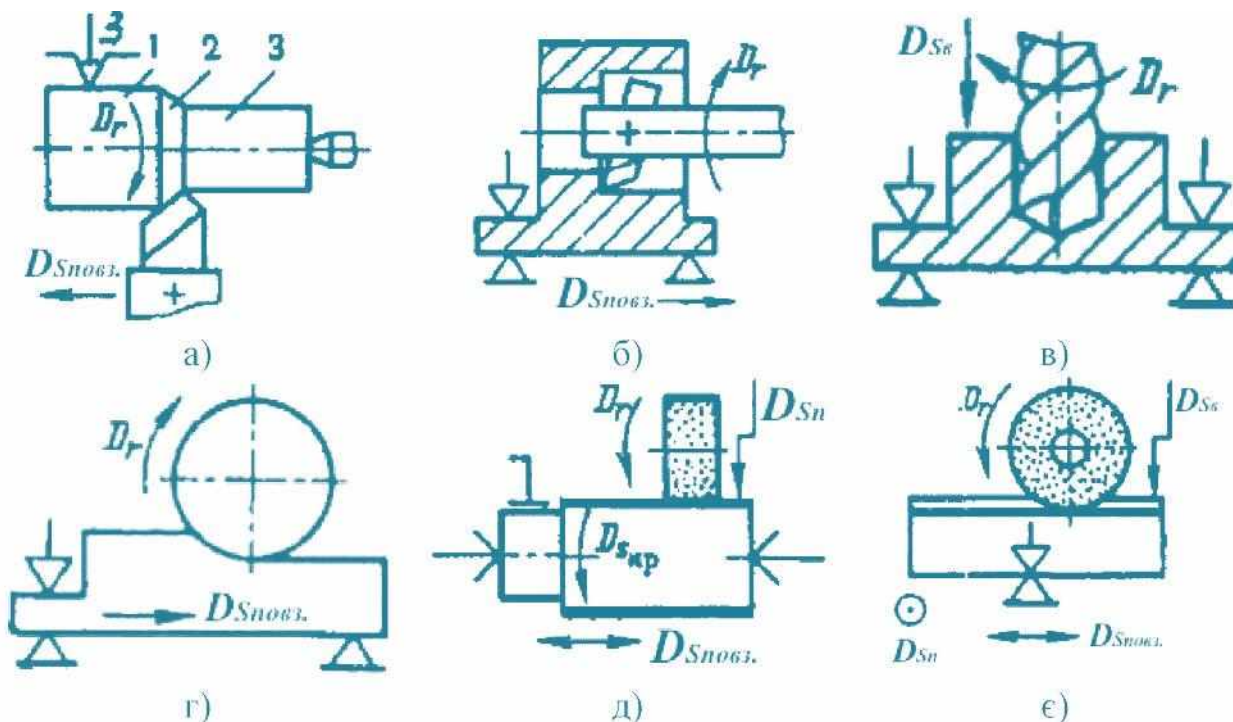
Схеми обробки заготовок: а)-точіння; б)-розточування; в)-свердління; г)-фрезерування; д)-шліфування на круглошліфувальному верстаті; е)-шліфування на плоскошліфувальному верстаті.
